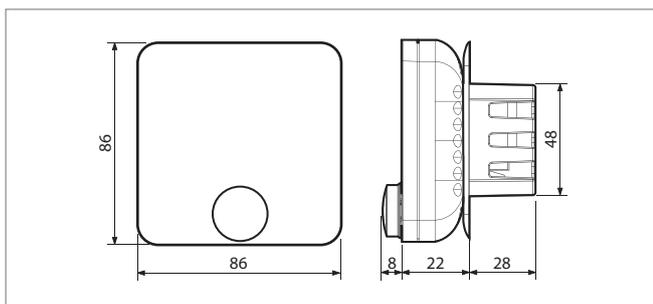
Dimensions pour l'élément de commande zone en cas de montage encastré (dimensions en mm)
